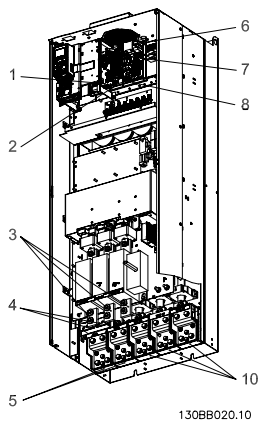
Compact IP 00 (Шасси) с разъединителем, плавким предохранителем и фильтром ВЧ-помех, размер корпуса E2
